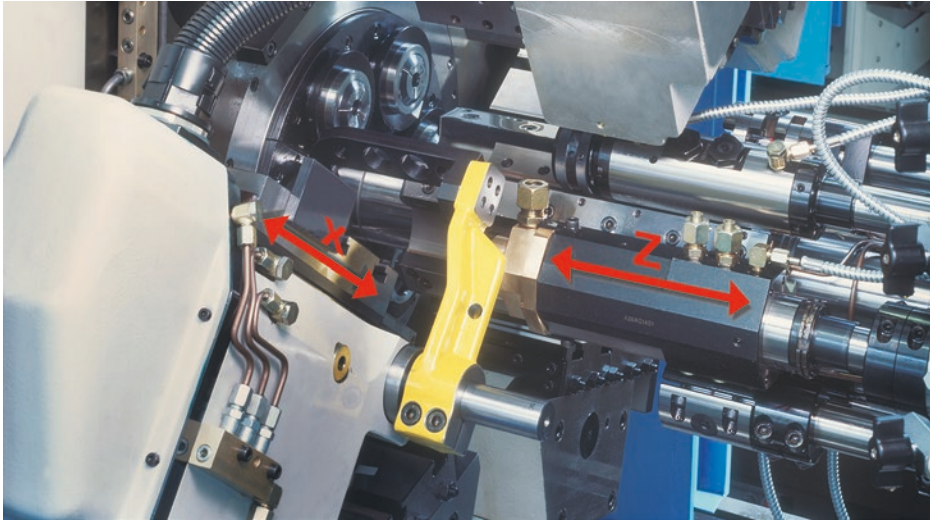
CNC-Abgreifspindel und rückwärtiger Bearbeitungsschlitten [Schu08]
